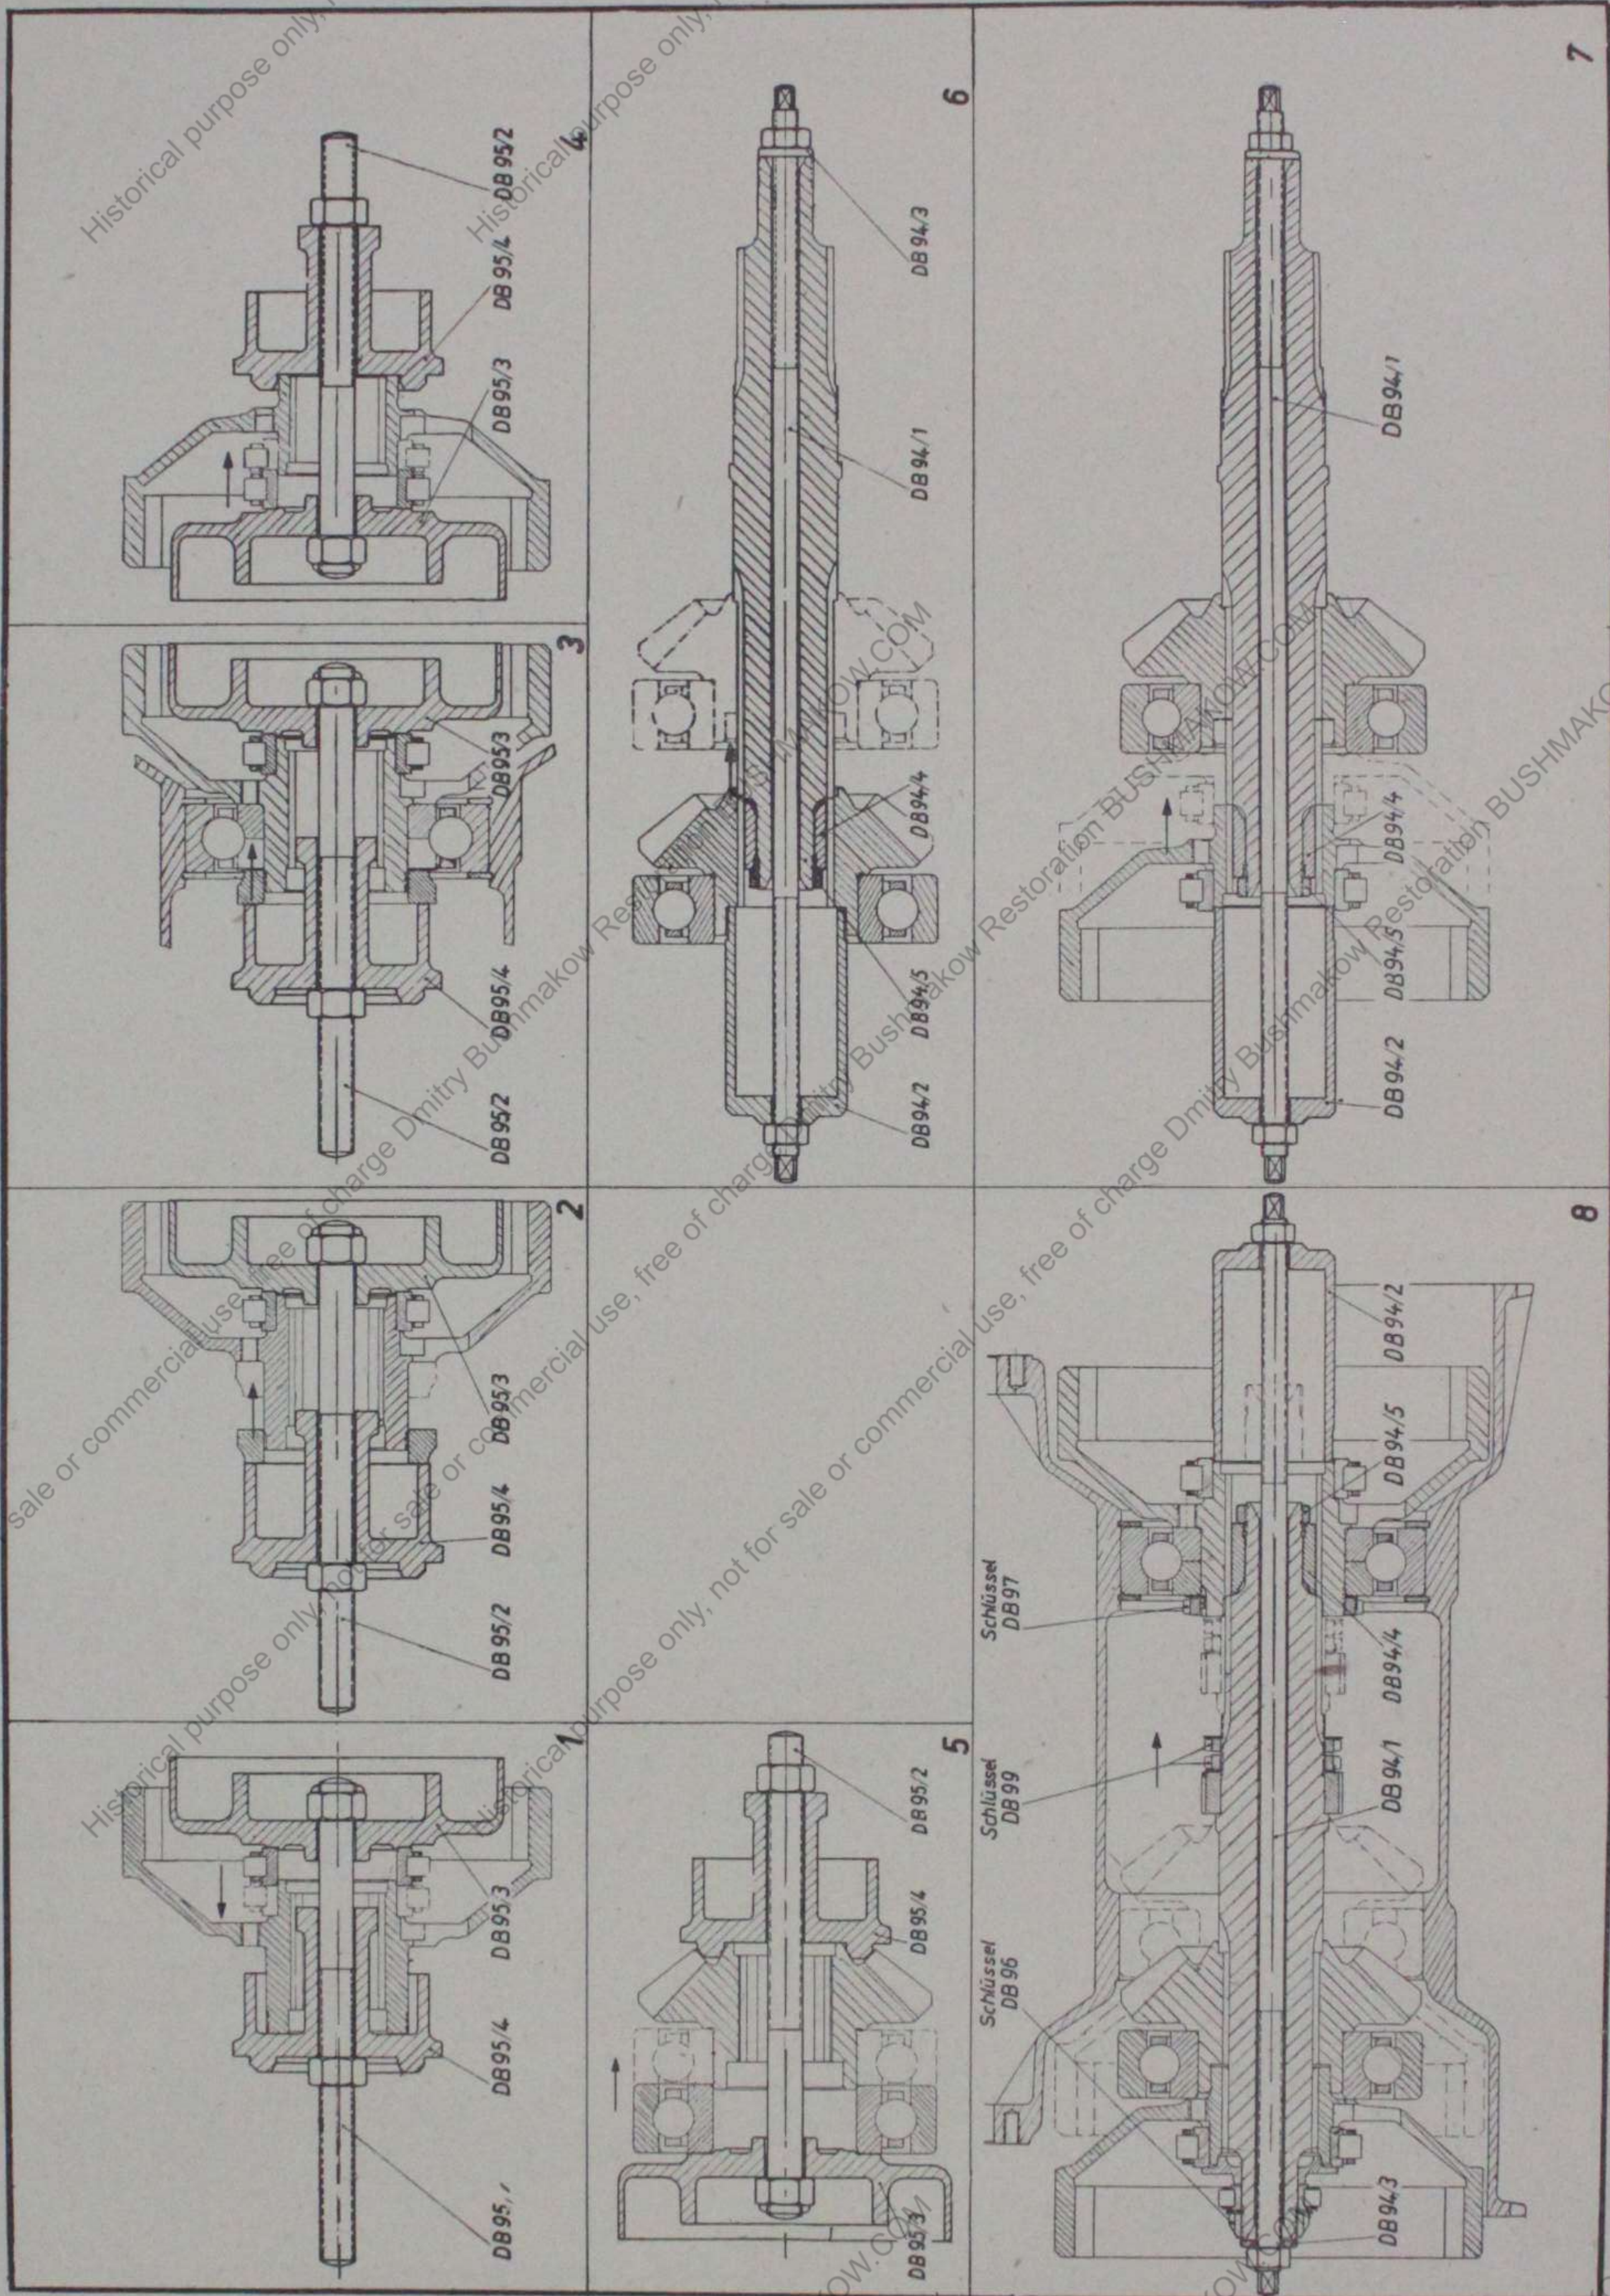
Rengetriebe mit Stüßbremse, Einbau
